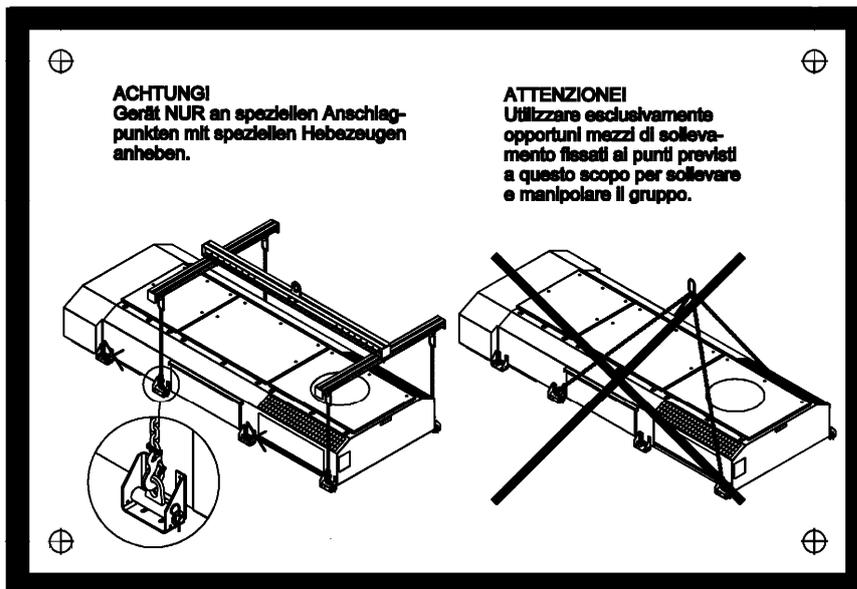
Targhetta con istruzioni di trasporto impianto di condizionamento vano passeggeri
